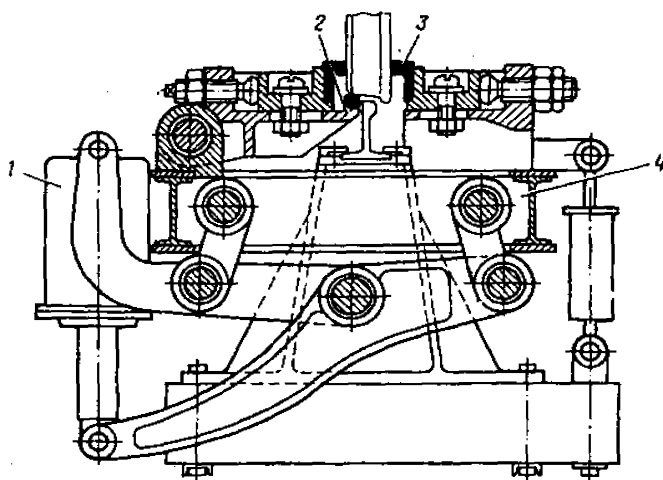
Кинематическая схема вагонного замедлителя КВ
